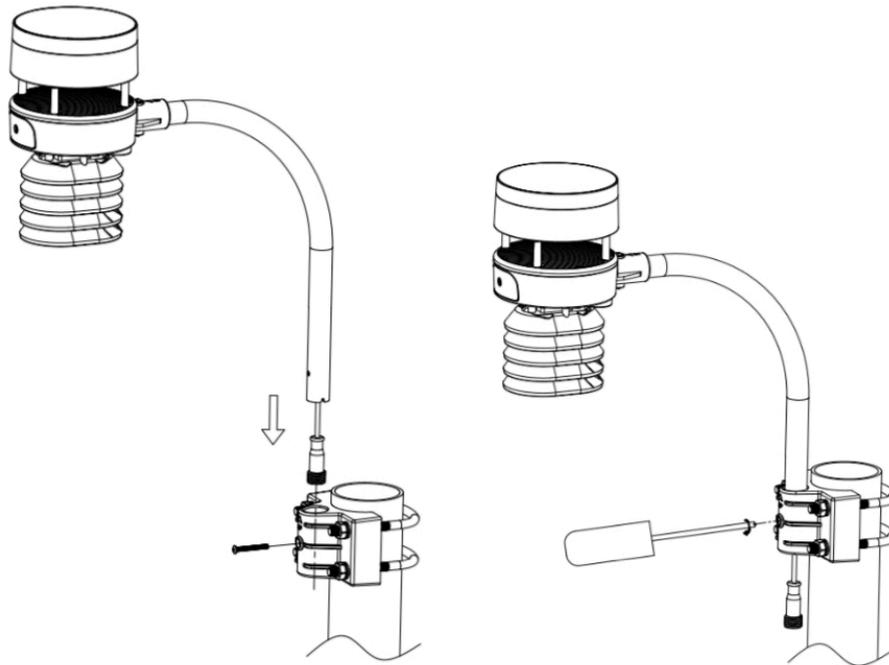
schema di montaggio del pacchetto del sensore 5-2
